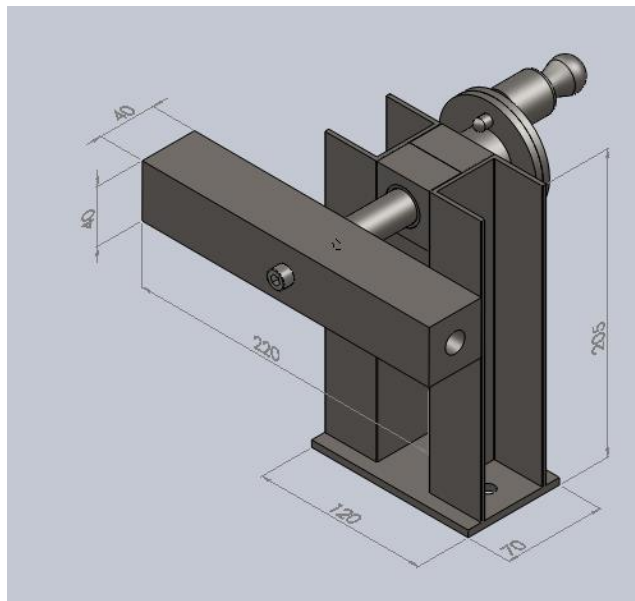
15. Soporte trasero potro de soldadura
